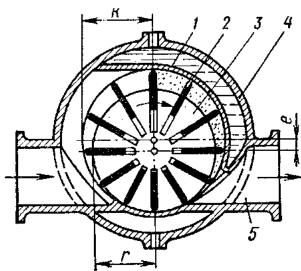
Схема роторного пластинчатого компрессора
